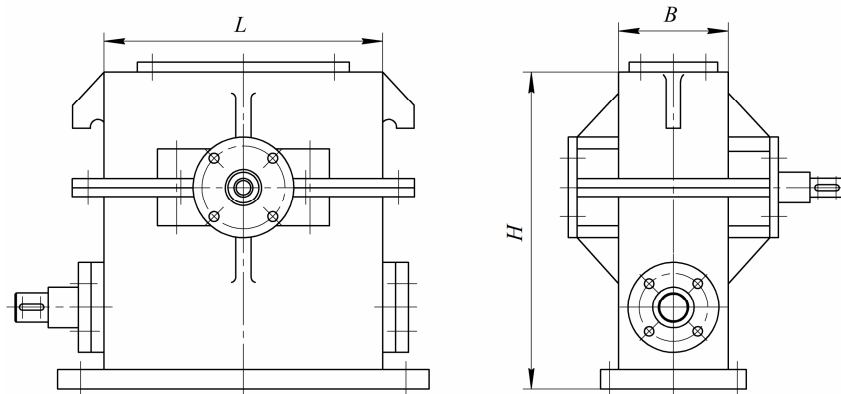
Компоновочный чертеж червячного редуктора
